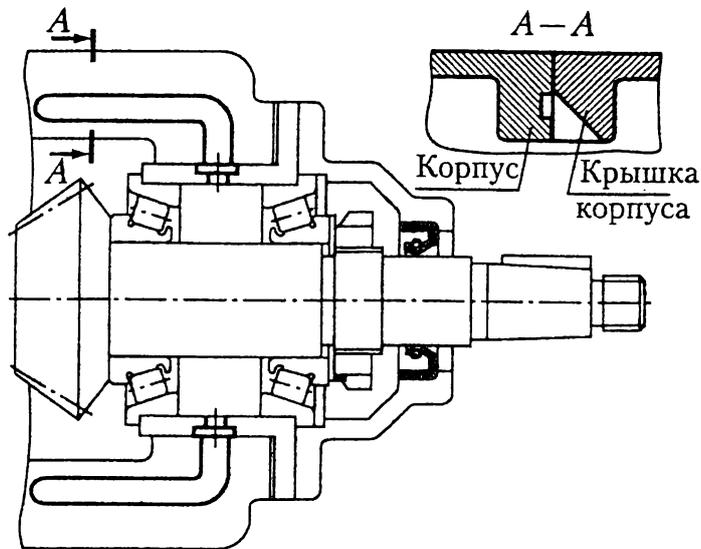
Вариант конструктивного решения облегчения смазывания подшипников вала конической шестерни [5]
